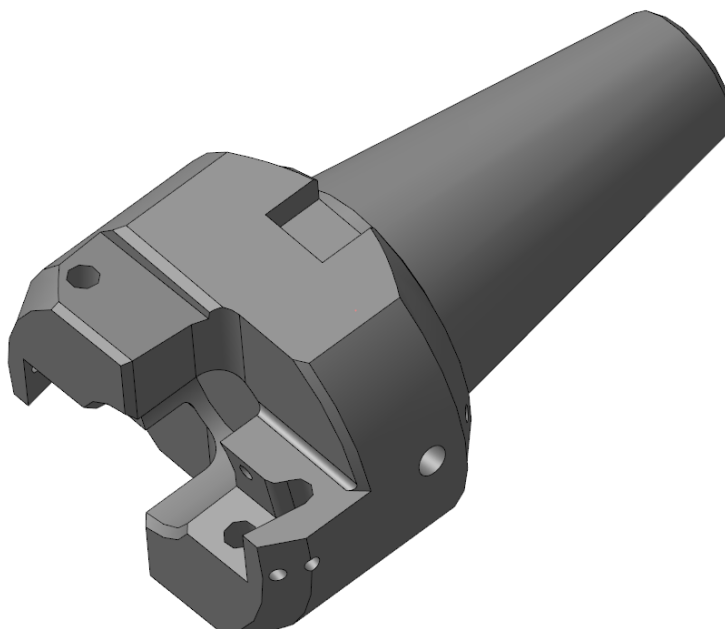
3-D модель корпусу інструментальної головки
